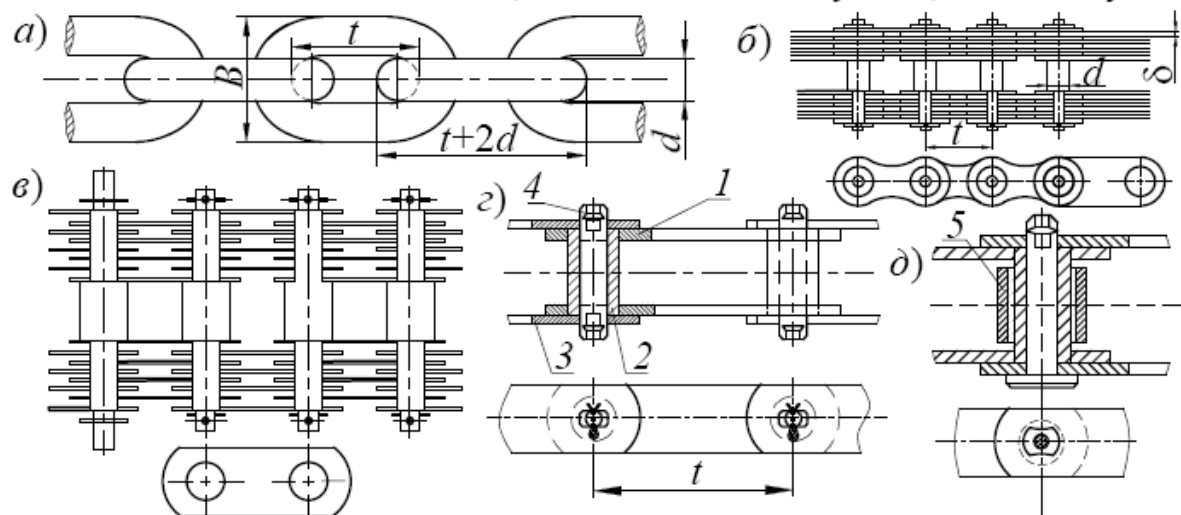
Цепи: а – сварная; б – безвтулочная пластинчатая с фигурными звеньями; в – грузовая пластинчатая с простыми звеньями; г – втулочная пластинчатая; д – втулочно-роликовая
